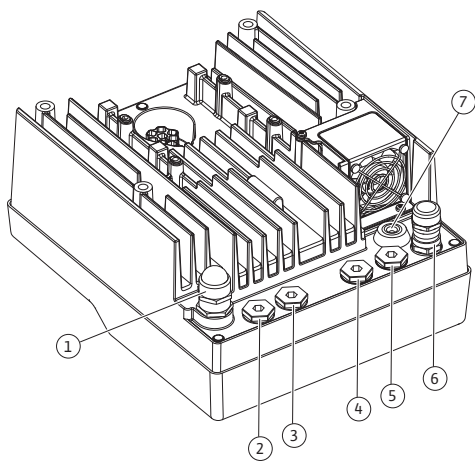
Presetupe pentru cablu/conexiuni de cablu
